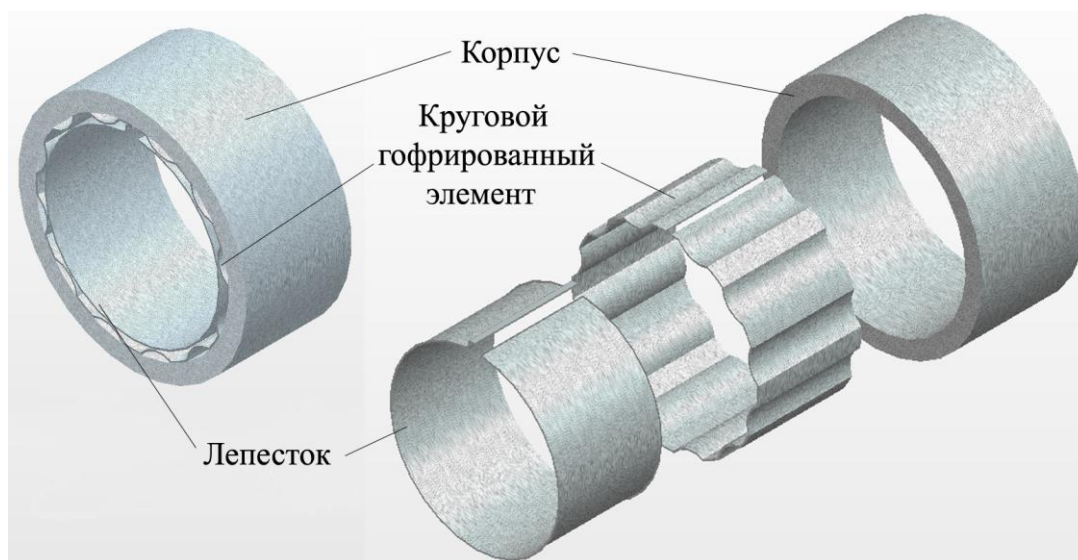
Лепестковый газодинамический подшипник с упругими элементами
